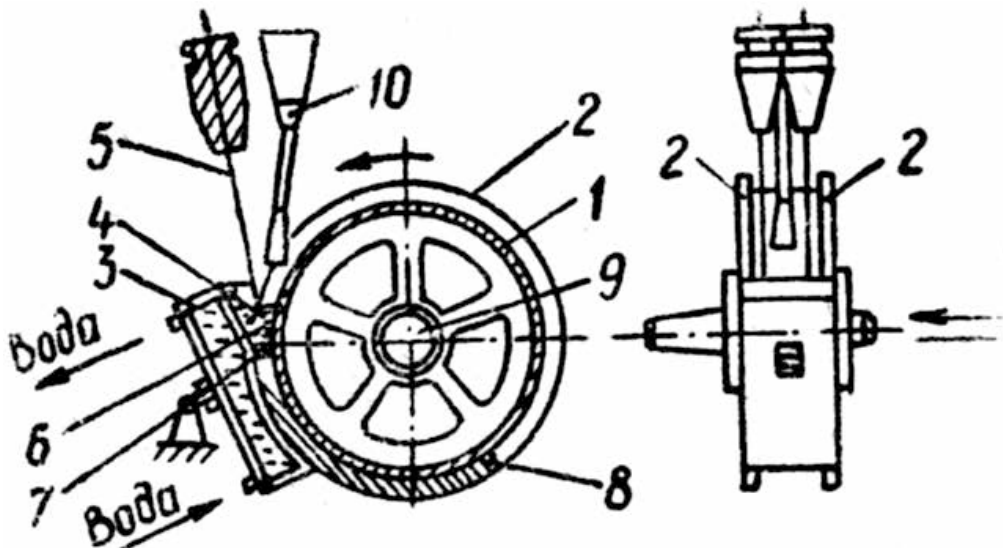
Електрошлакове наплавлювання: *1* – наплавлювана деталь; *2* – габаритні диски; *3* – кристалізатор; *4* – флюс; *5* – електрод; *6* – шлакова ванна; *7* – ванна
